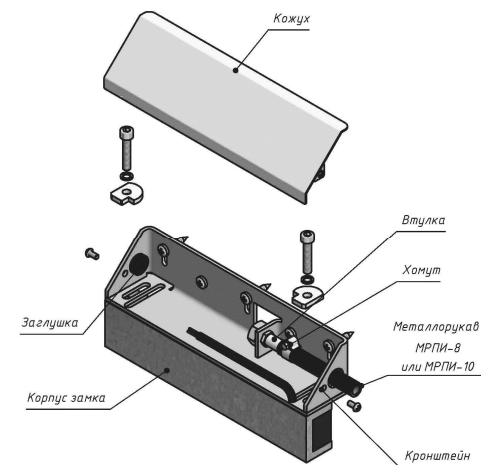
Крепление корпуса замка с помощью комплекта МК AL-350FB-M-02 для прокладки кабеля в металлорукаве
